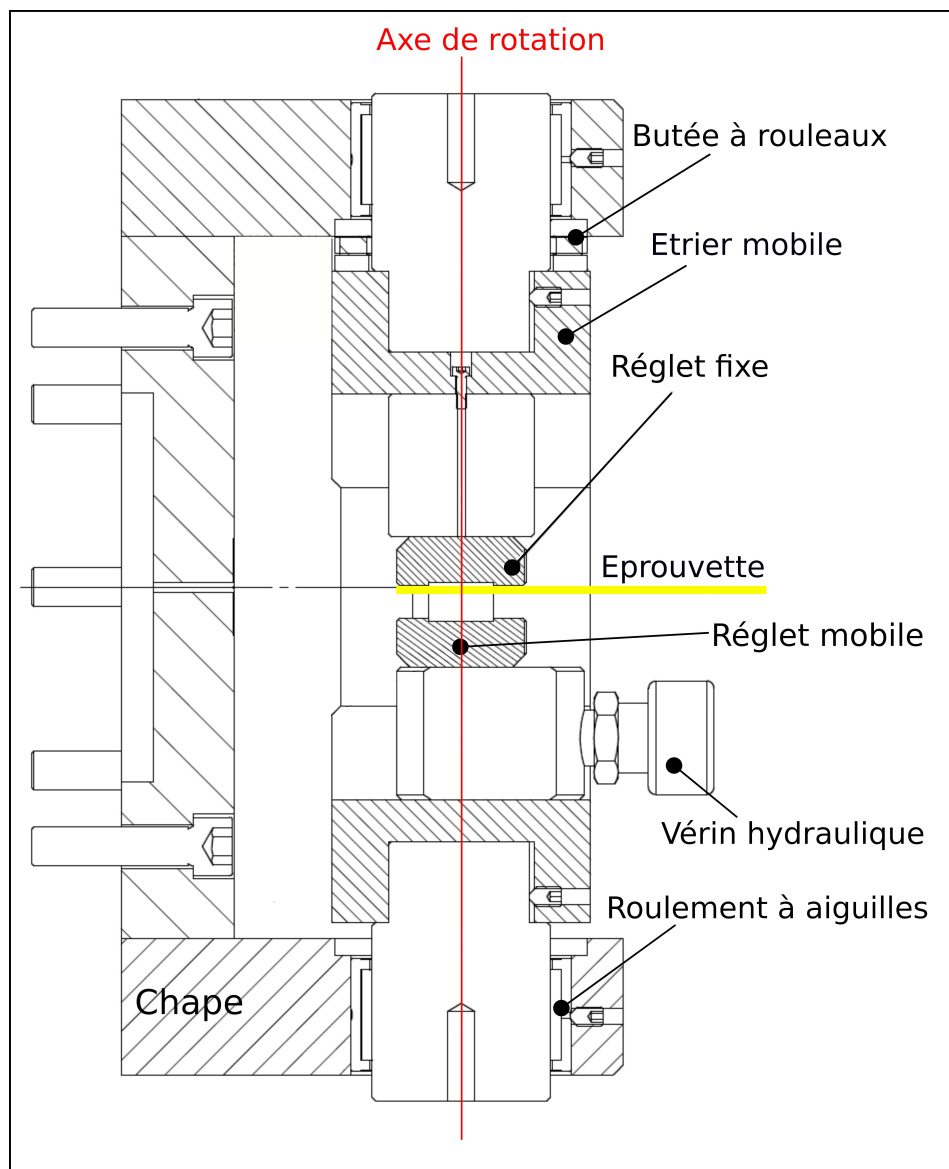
Vue en coupe du mors hydraulique articulé de la machine biaxiale
